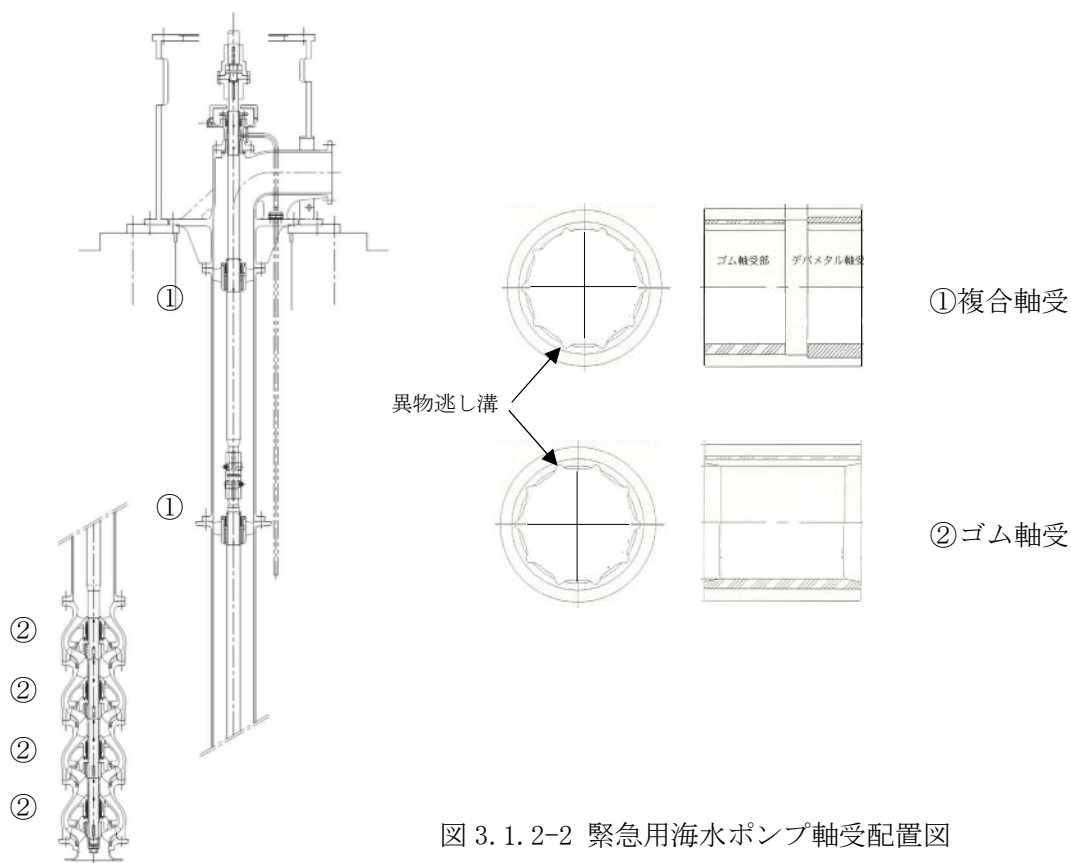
緊急用海水ポンプ軸受配置図
